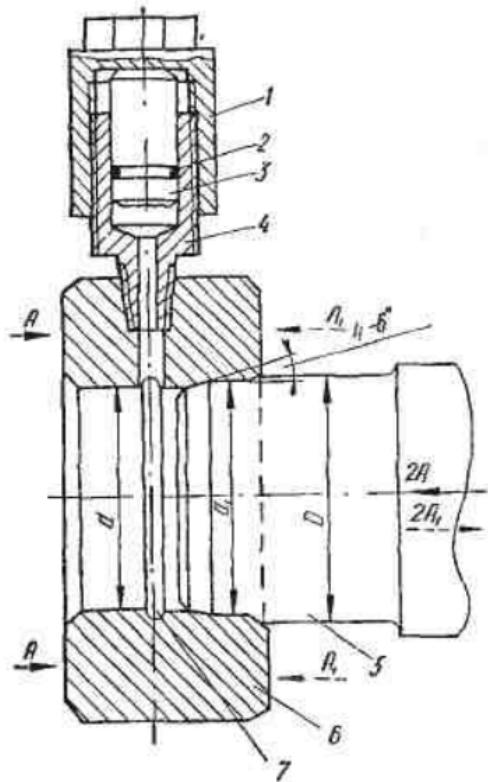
Схема соединений деталей посадкой с натягом и гидравлического приспособления для распрессовки:
